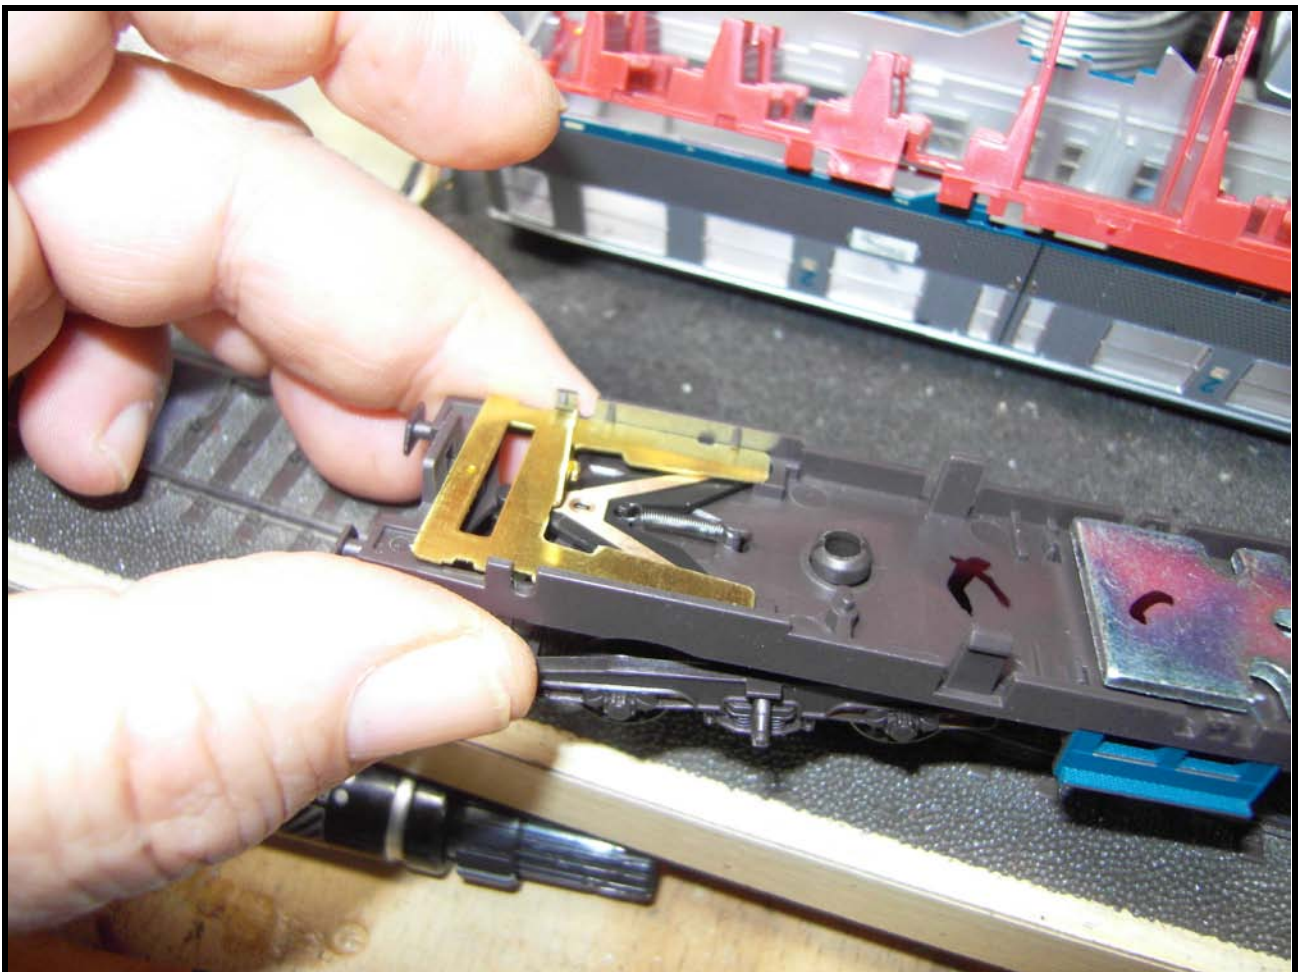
sopra la molletta la piastra scorre ed è oramai in posizione corretta
